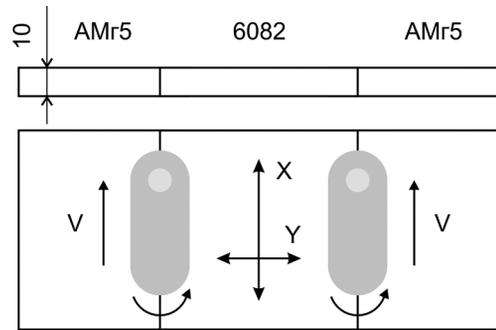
Условная схема сварки стыковым швом биметаллического соединения AMg5 - 6082 - AMg5
